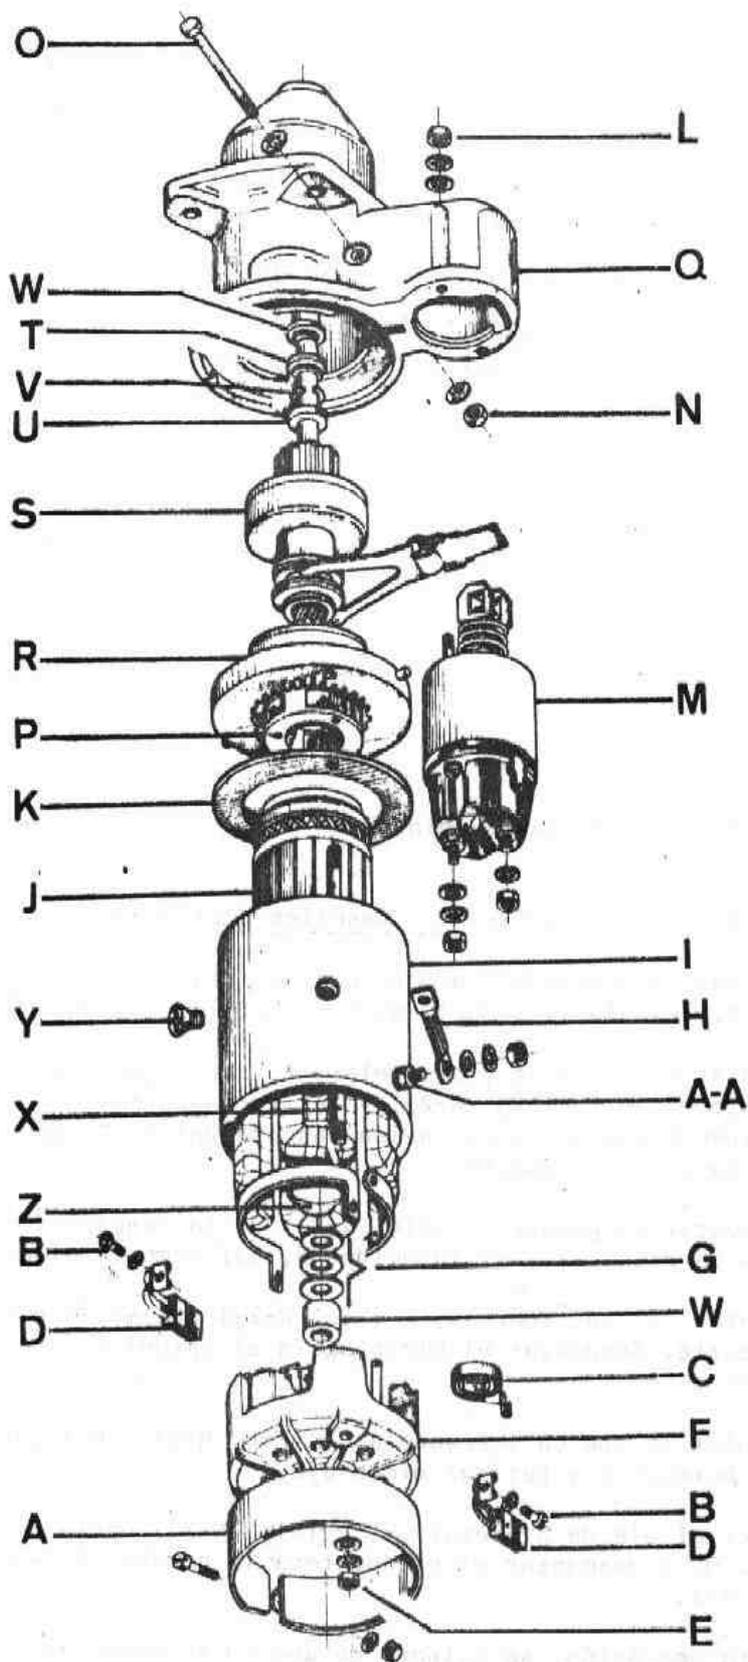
Despiece del motor de arranque MIRE-12.9 para motores Diesel y Gasolina 3 1/2 L.
